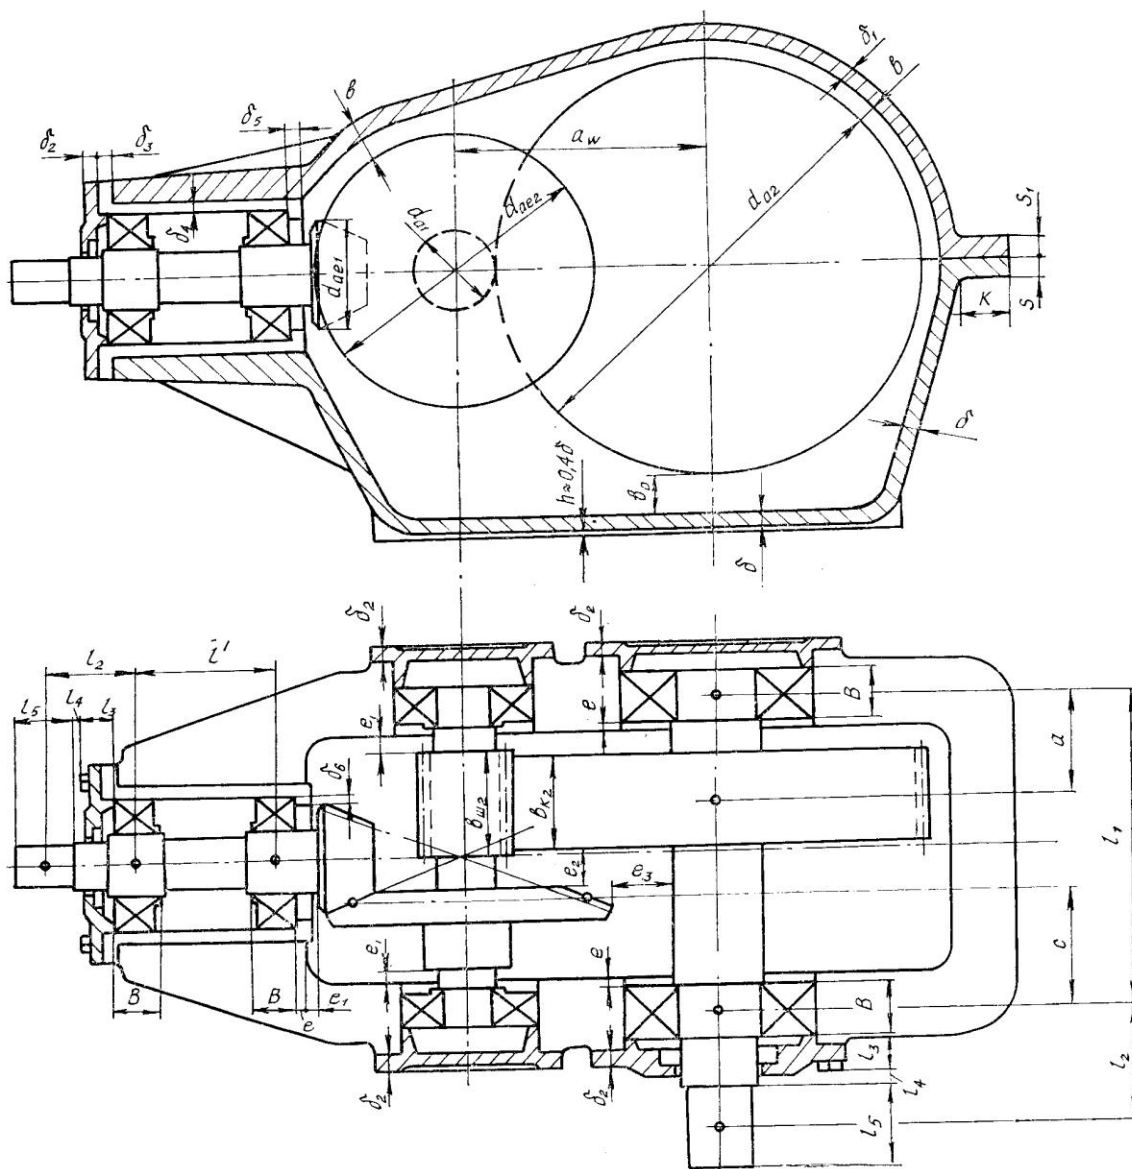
Компонувочне креслення конічно-циліндричного редуктора
